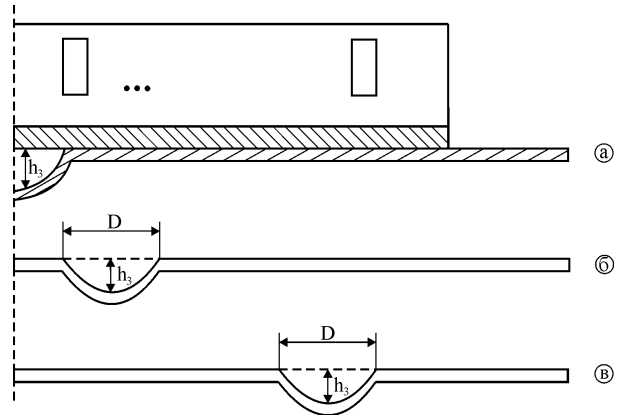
Розрахункова схема багатовиткового індуктора із допоміжним екраном та заготовки із вм'ятинною
